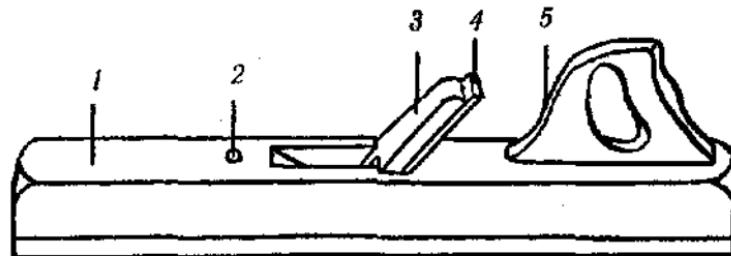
Фуганок: 1 — колодка; 2 — пробка; 3 — клин; 4 — нож; 5 — ручка.
